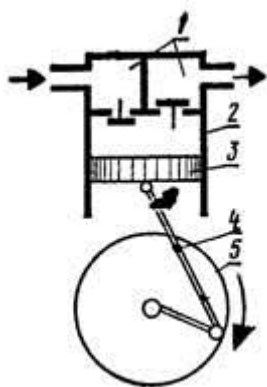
Схема работы поршневого компрессора 1-клапаны; 2- цилиндр; 3-поршень; 4- шатунно-кривошипный механизм; 5- маховик
